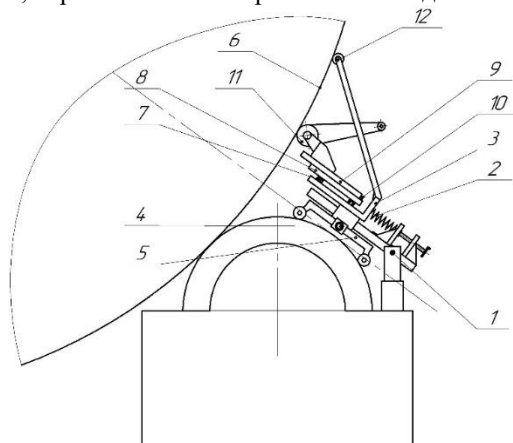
Станок для обработки бандажей: 1- шарнир; 2- пружина; 3- кронштейн; 4- шарнир; 5- роликовая опора; 6- бандаж; 7- сдвоенные рельсовые направляющие качения; 8- продольный суппорт; 9- каретка; 10- регулировочный винт; 11- обрабатывающий узел; 12- копирующий ролик [7]
